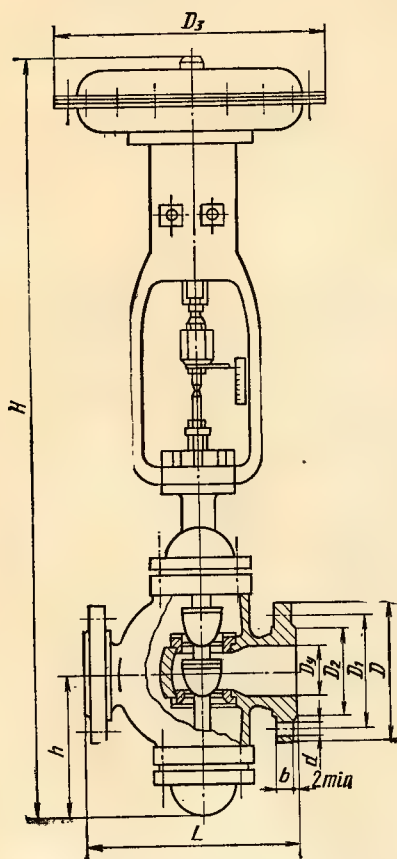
Регулирующий клапан ЦКБА с мембранным приводом
